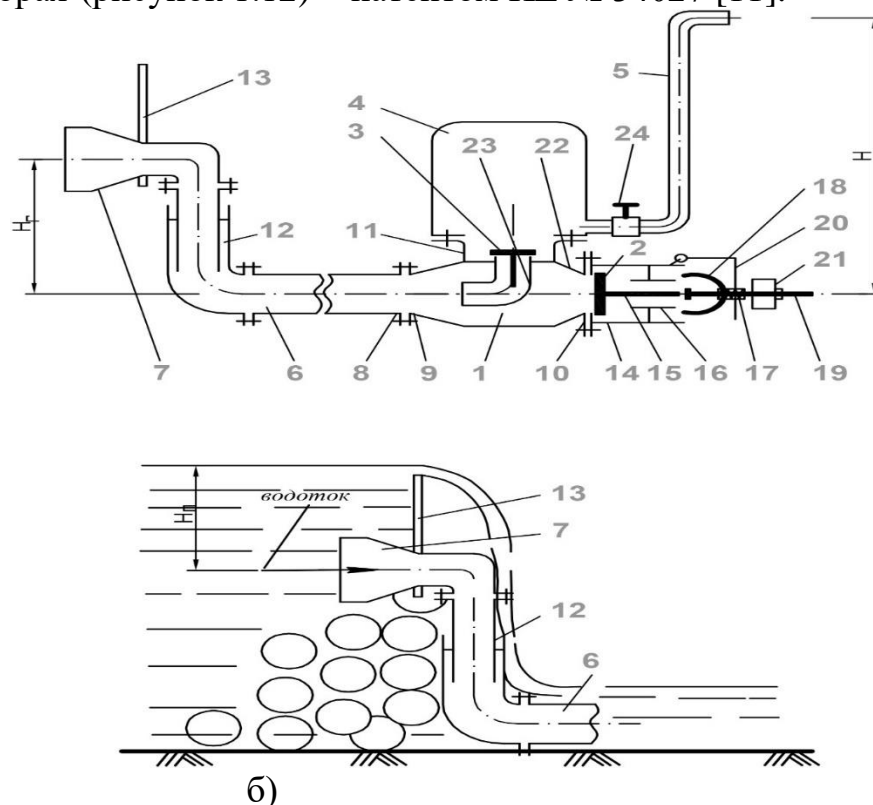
Конструктивно-технологическая схема напорно-вакуумной насосной установки конструкции КазНАИУ
